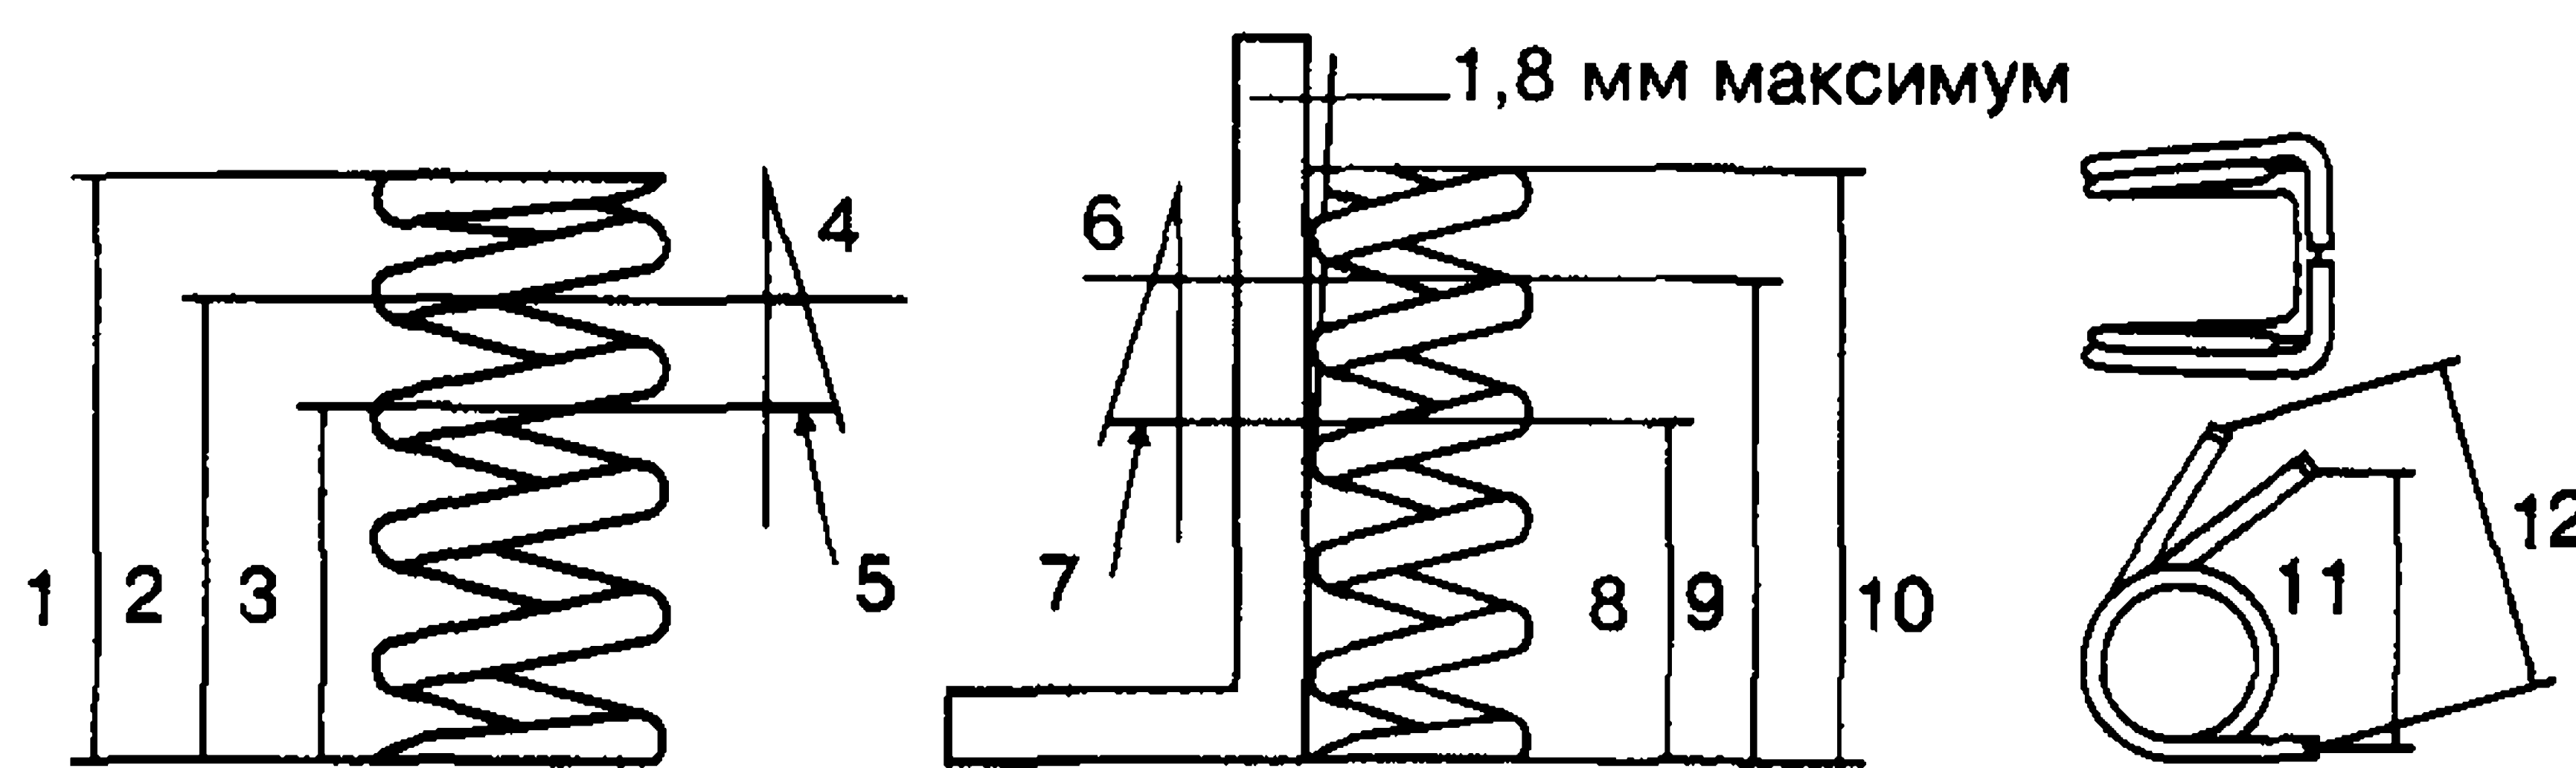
Дефектовка пружин клапанов и рычагов (см. табл. 9)
